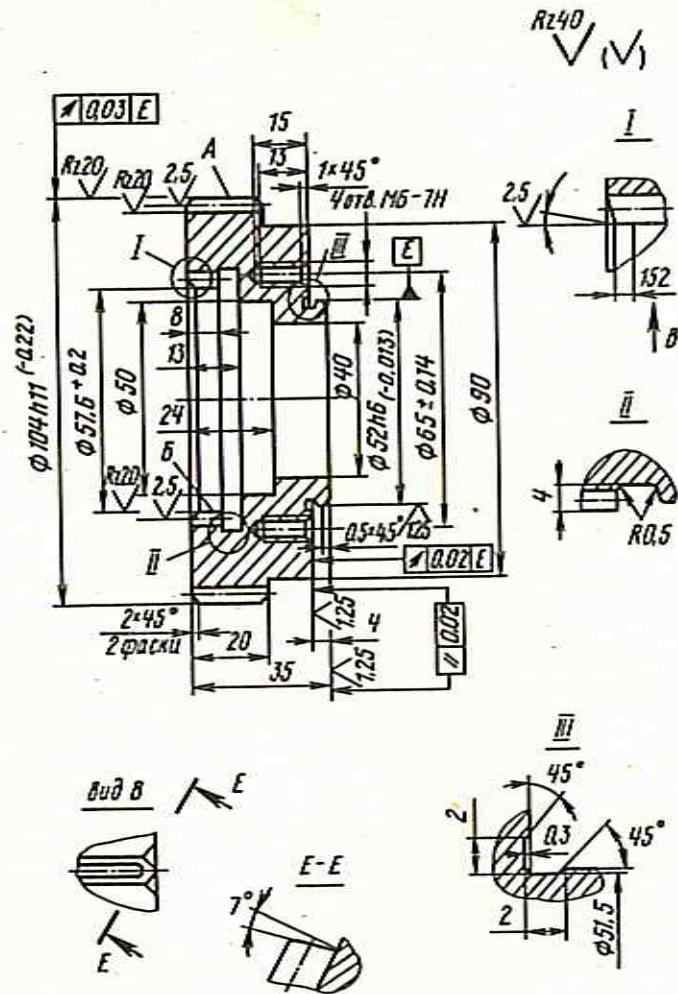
Колесо зубчатое, деталь № 3Л722А.322.401 НРС 22..30
